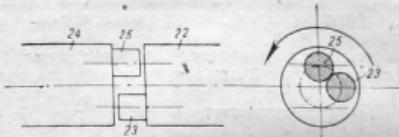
Полуавтомат Волтам для фрезеровки анкерных колод.
